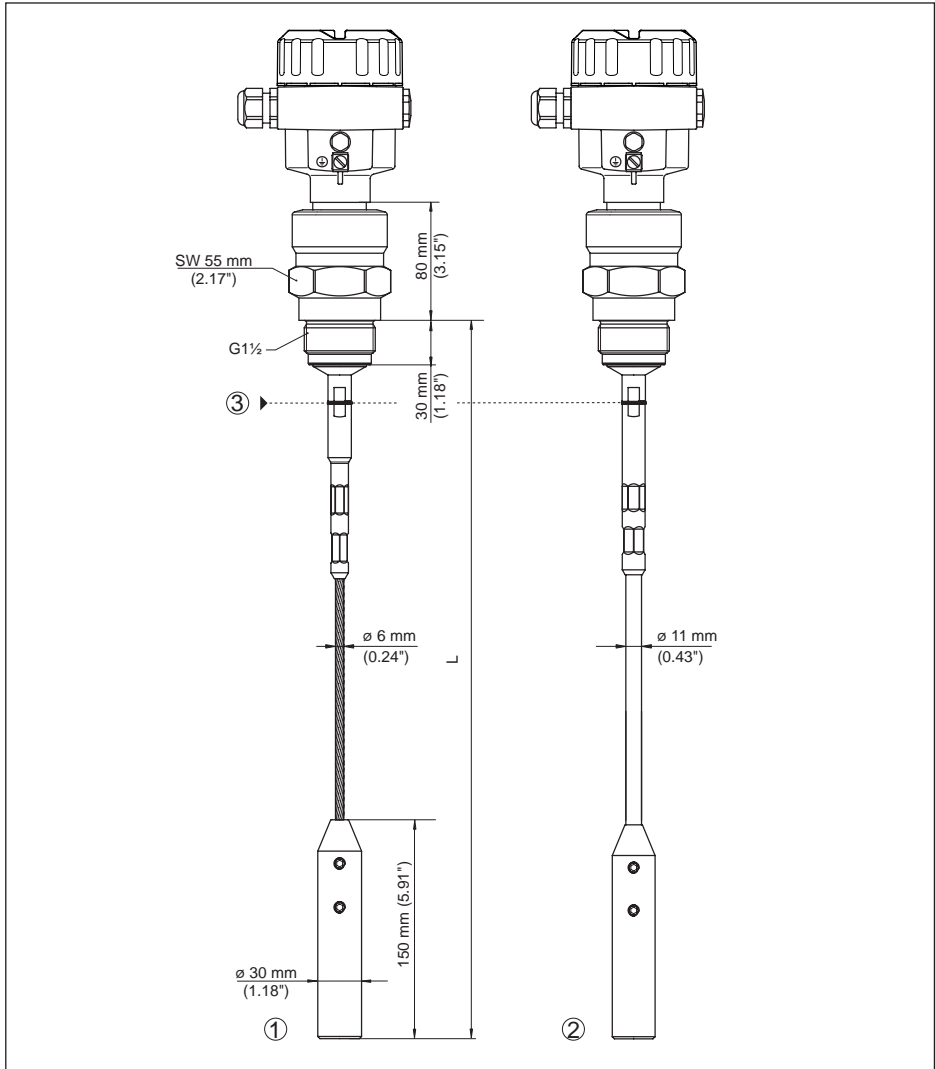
NivoGuide 3100, трос $\varnothing 6$ mm (0.236 in), $\varnothing 11$ mm (0.433 in), резьбовое исполнение, с натяжным грузом (все натяжные грузы с резьбой M12 для рым-болта)
